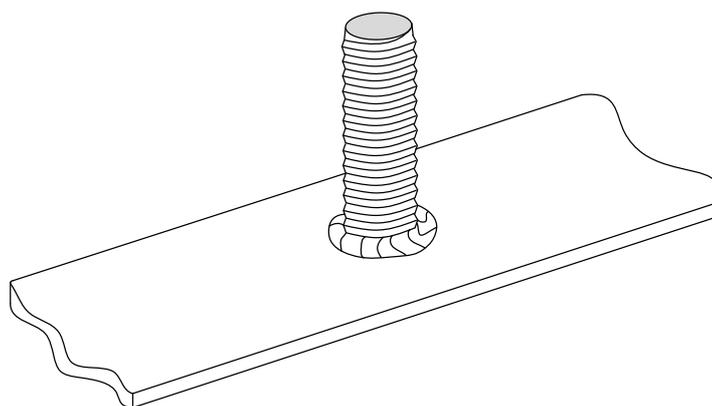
Сварное соединение болта крепления проводников заземления к ГЗШ
